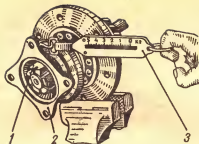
Проверка затяжки подшипников вала ведущей шестерни автомобиля типа ГАЗ:
